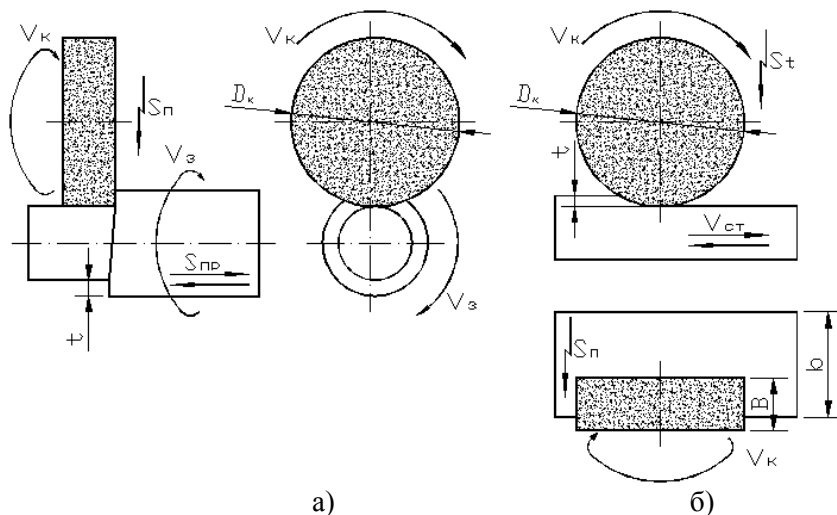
Схема шлифования поверхностей и элементы резания при шлифовании:
